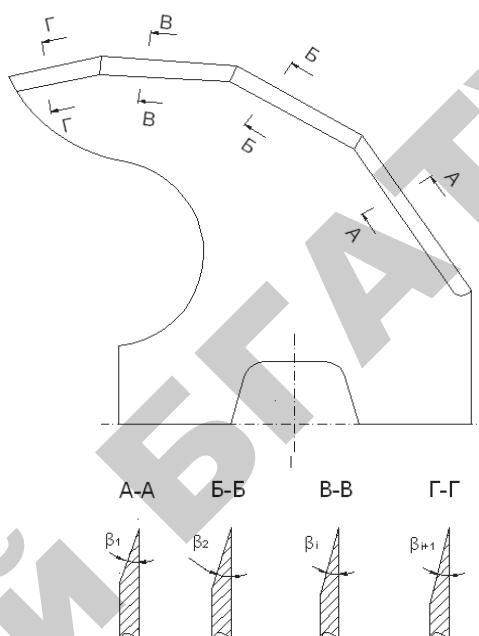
Схема куттерного ножа с изменяющимся углом заточки режущей кромки
